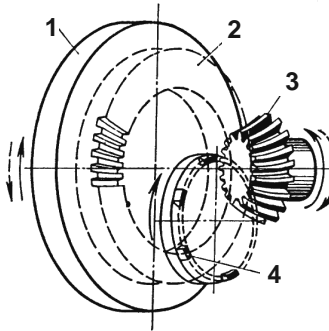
Нарізання конічних коліс із криволінійними зубами:
